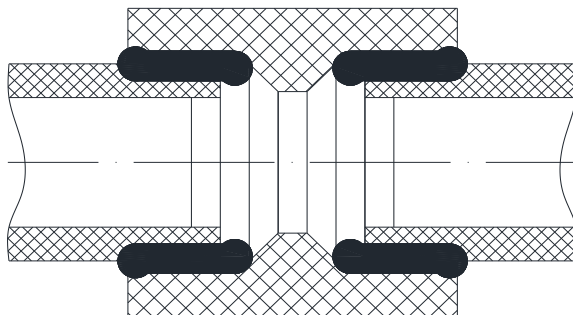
Конструктивные элементы шва сварного соединения (шов Н2)
